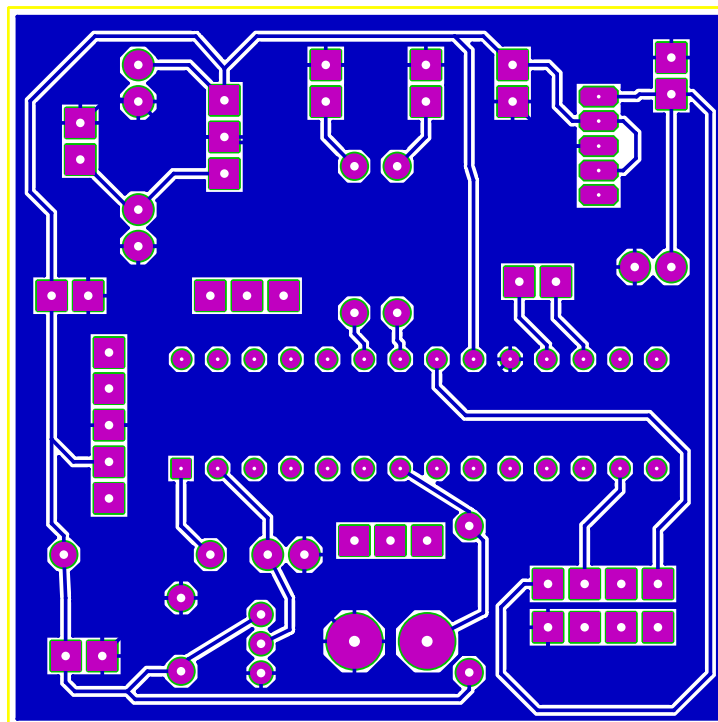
Desenho da PCB, *bottom layer* - “Módulo reboque”
